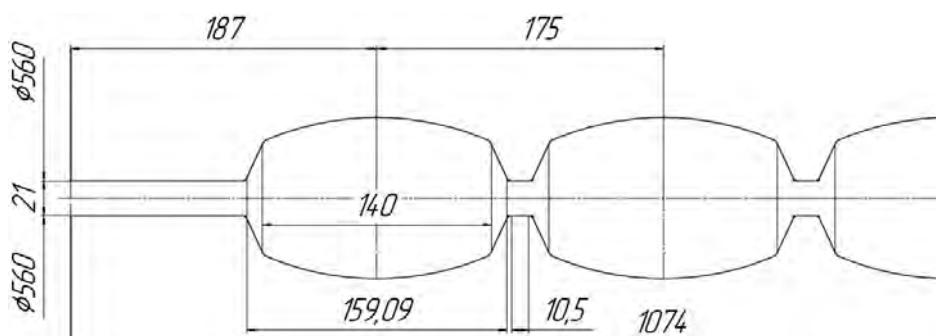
Предлагаемая компоновка калибров на бочке вала № 1
